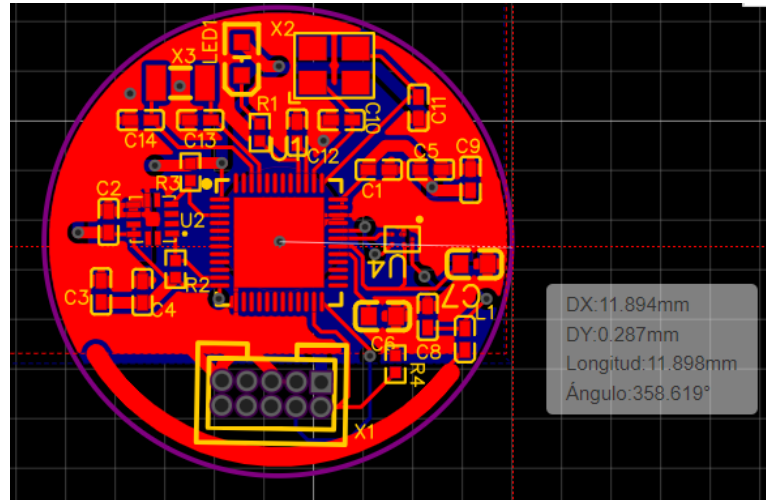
Diseño de PCB de BLE\_PCB\_V2
